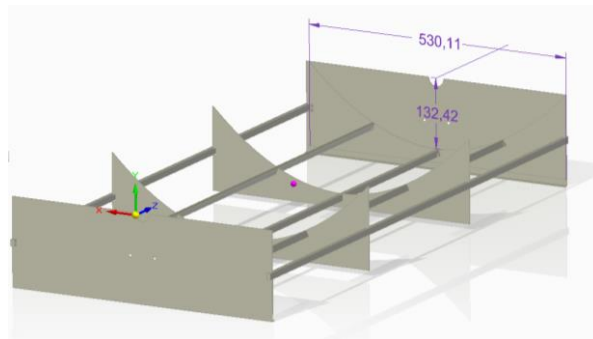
Estructura del canal parabólico. Fuente: elaboración propia
